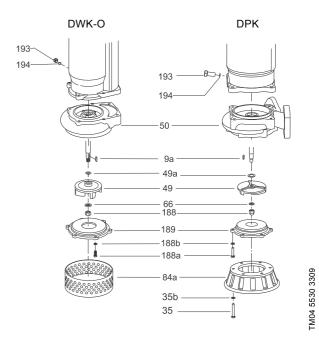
Демонтаж корпуса насоса и рабочего колеса
